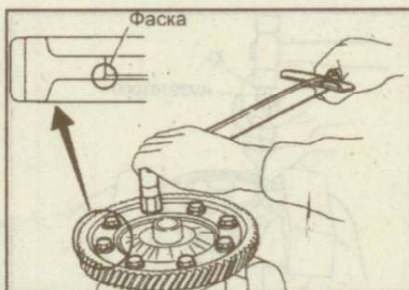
Затягивание болта крепления ведомой шестерни главной передачи к коробке дифференциала
